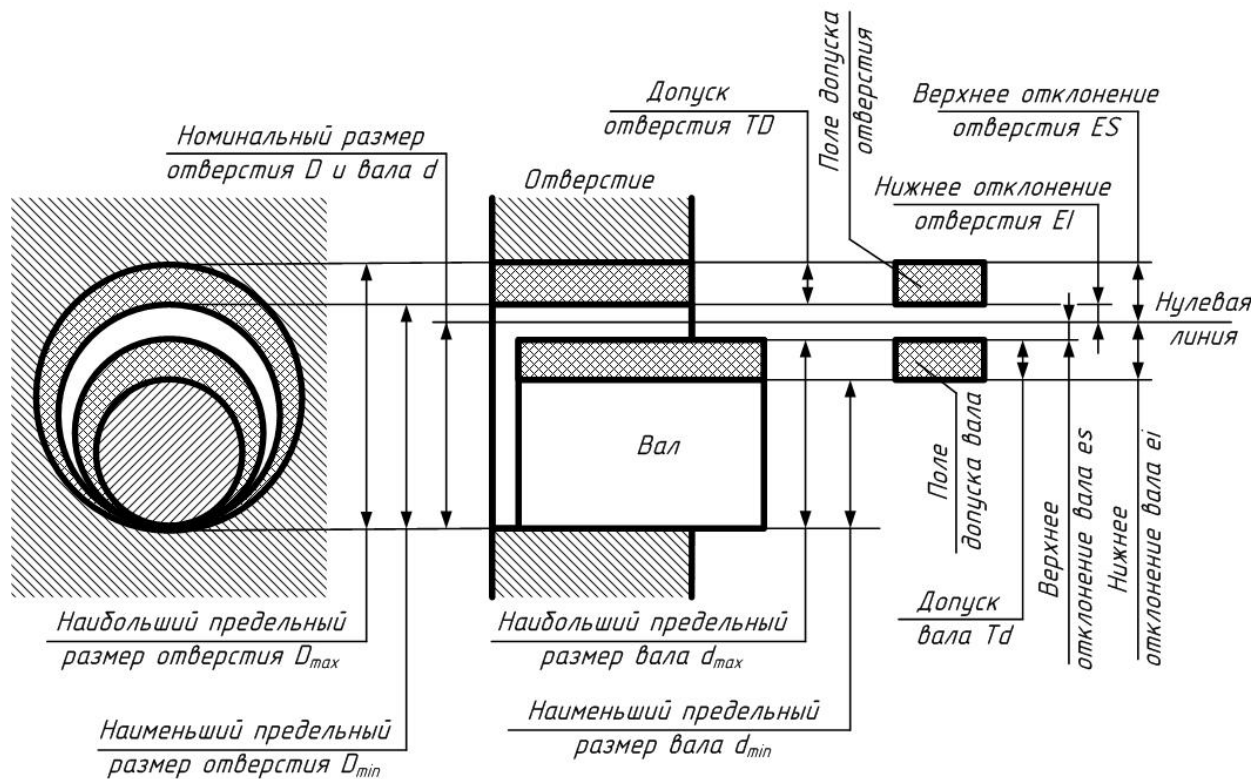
Графическое представление размеров, отклонений и допусков отверстия и вала
